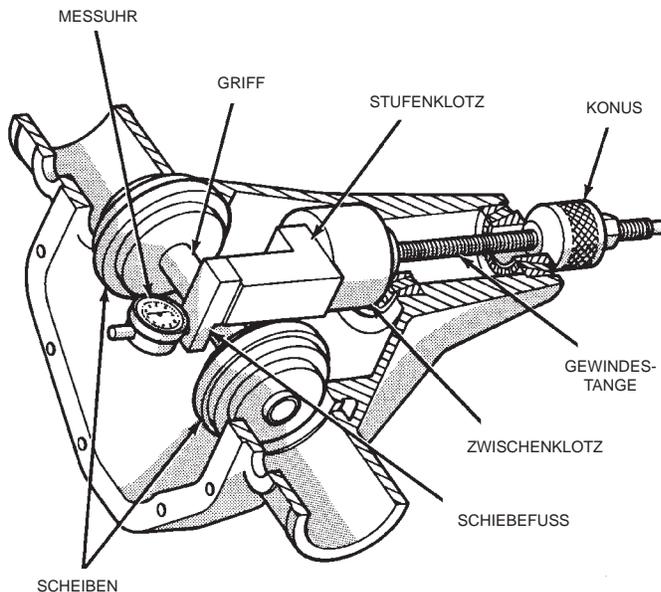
Spezialwerkzeuge zum Messen der Tiefe des Antriebskegelrads
